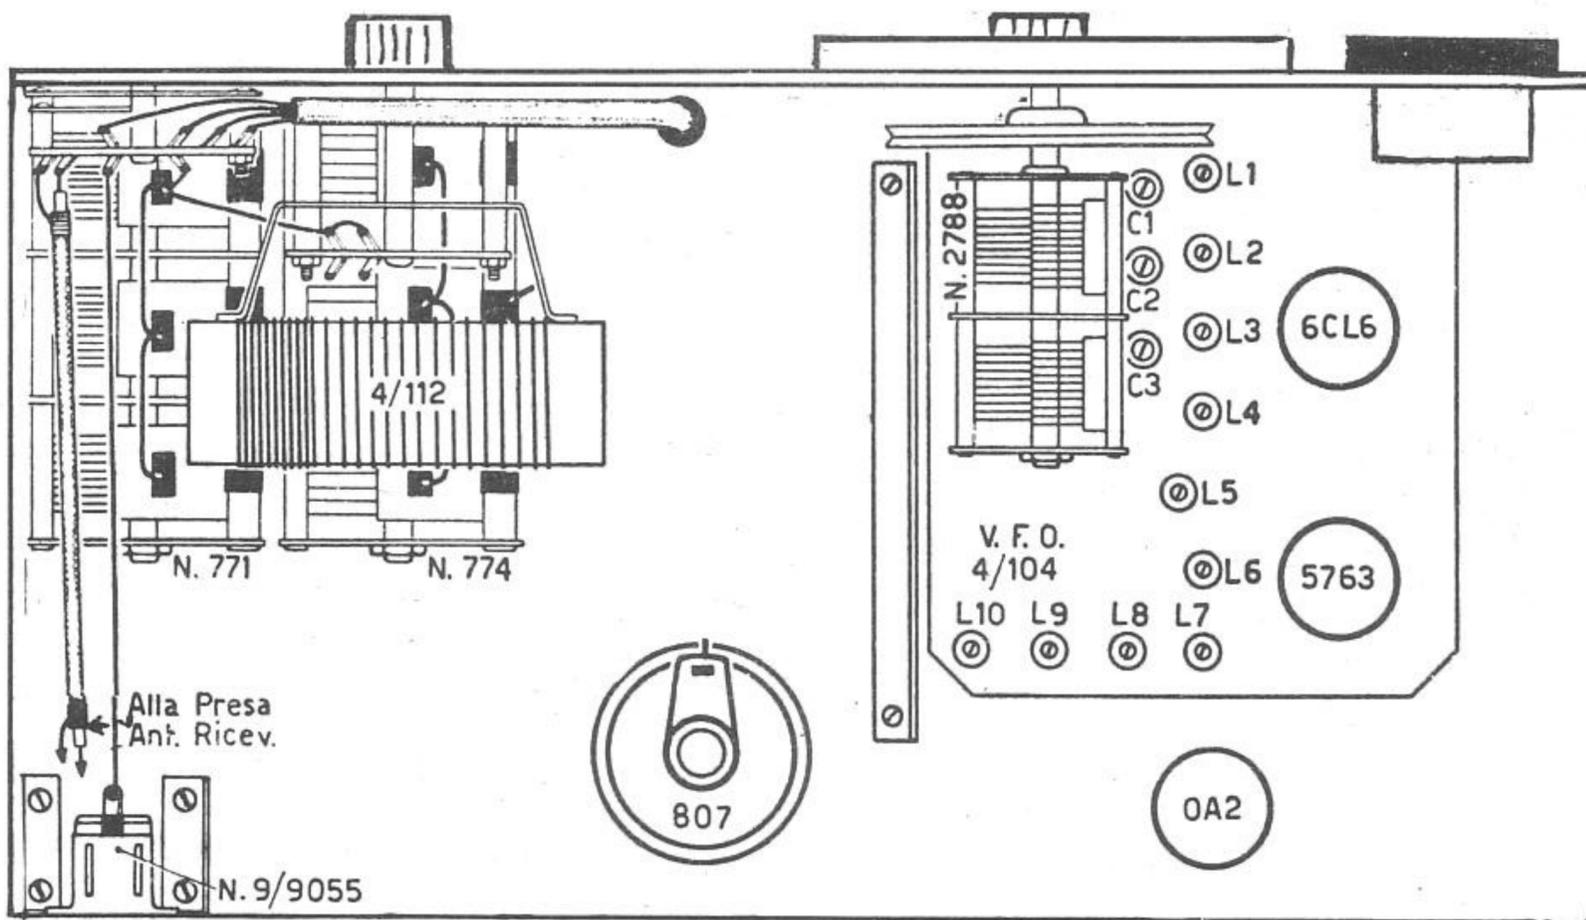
Exemple de disposition des composants sur un châssis. Les deux instrument (milliampèremètres) de plaque et de grille, peuvent être montés l'un à côté de l'autre, sur le côté gauche (vu d'en face) du panneau, comme l'indique la figure (l'appareil étant vu d'en haut, l'un des deux milliampèremètres est visible). En tous cas, étant donné les fréquences élevées de fonctionnement, les connexions doivent être, autant que possible, courtes. L'alimentation et l'éventuel modulateur doivent être montés, de préférence, sur des châssis séparés; l'ensemble tout entier peut être monté sur une table unique ou, mieux encore, sur un « rack » vertical.
